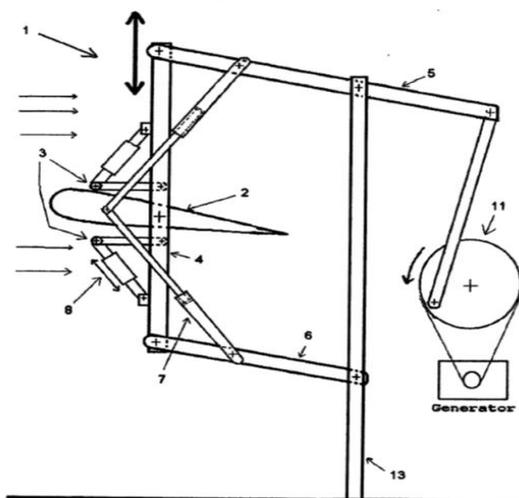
Конструкция ветродвигателя с возвратно-поступательным устройством
